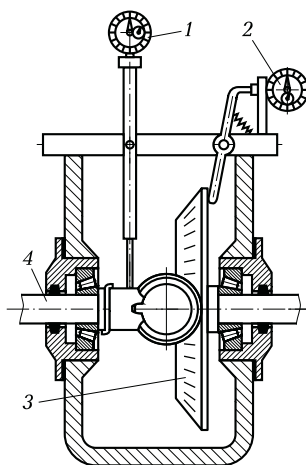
Схема контроля сборки конических зубчатых передач:
